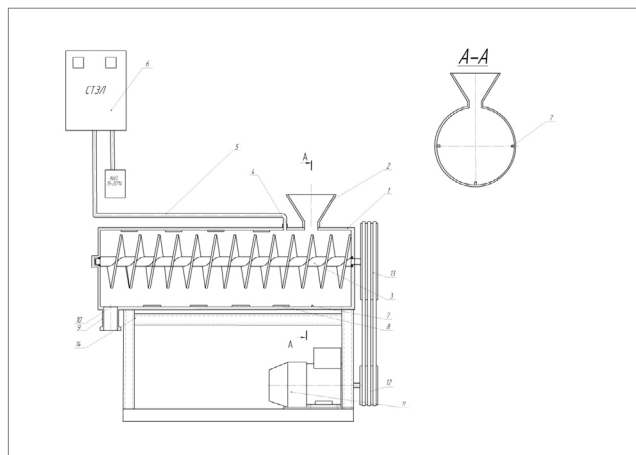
Установка для обеззараживания зерна: 1 – корпус цилиндрический, 2 – загрузочный бункер, 3 – шнек, 4 – штуцер, 5 – трубопровод, 6 – установка СТЭЛ, 7 – форсунки, 8 – ультразвуковые излучатели, 9 – выгрузной патрубок, 10 – задвижка, 11 – мотор-редуктор, 12 – ведущий шкив, 13 – ведомый шкив, 14 – опора.
